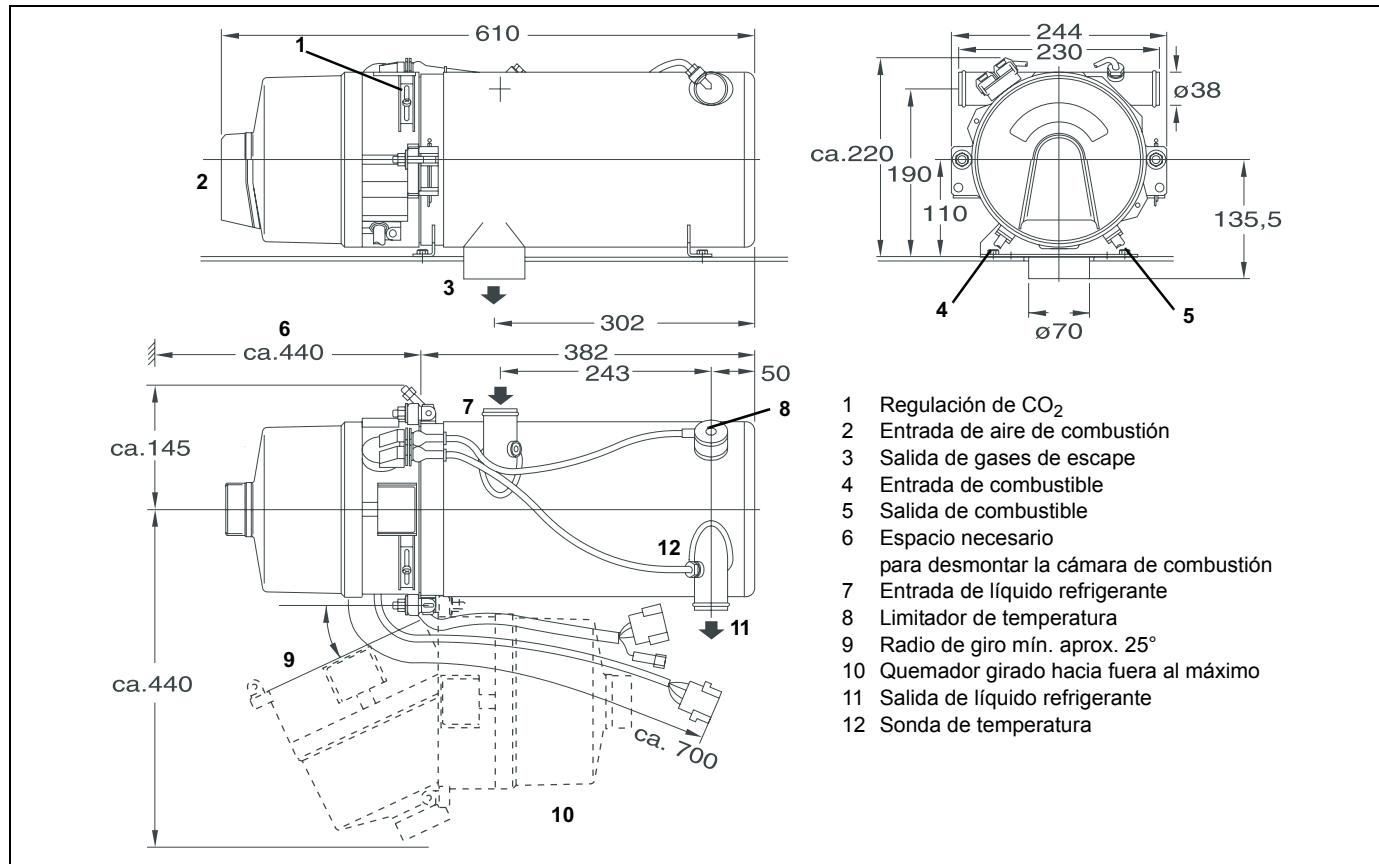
Dimensiones del calentador Thermo 230 / 300 / 350 (montaje horizontal)
